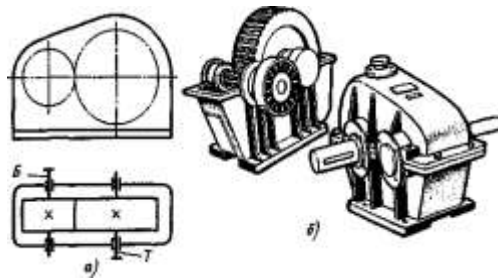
Одноступенчатый горизонтальный редуктор с цилиндрическими зубчатыми колесами:
